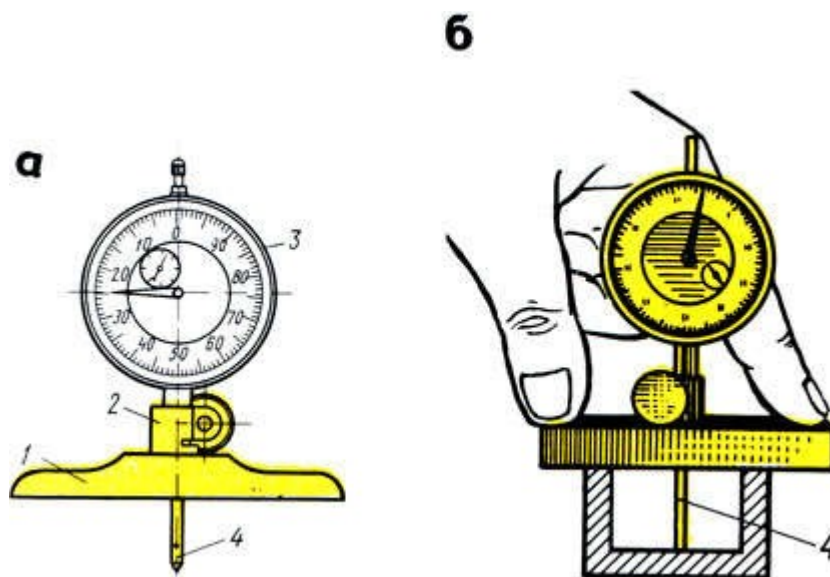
Индикаторный глубиномер: а - устройство, б - прием проверки; 1 - основание, 2 - державка, 3 - индикатор, 4 - измерительный стержень
